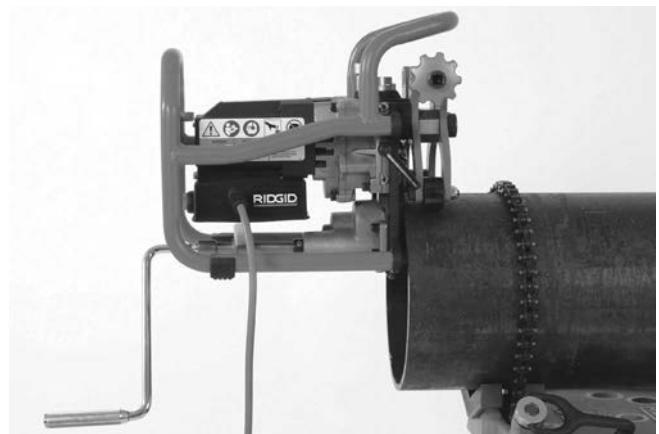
Станок для снятия фаски, установленный на заготовке
